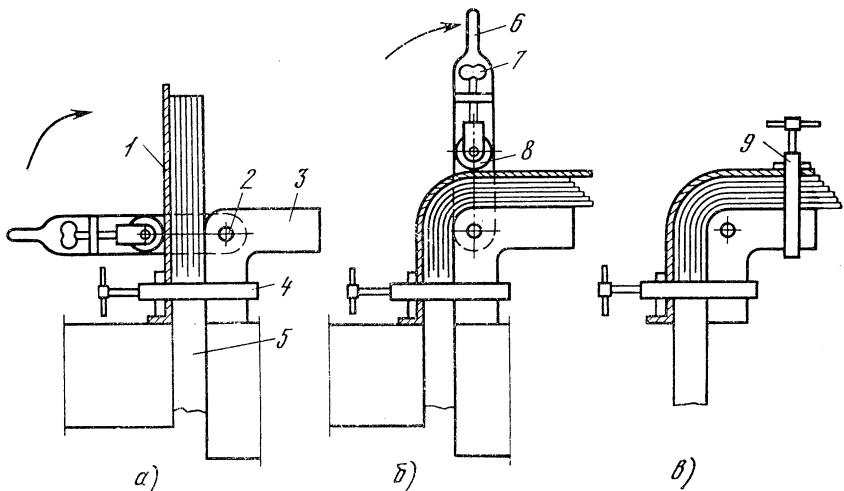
Приспособление для склеивания гнутопропильных заготовок из древесины:
